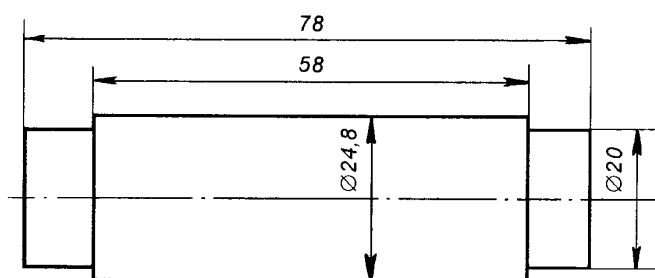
Оправка для запрессовки поршневого пальца в поршень и шатун
